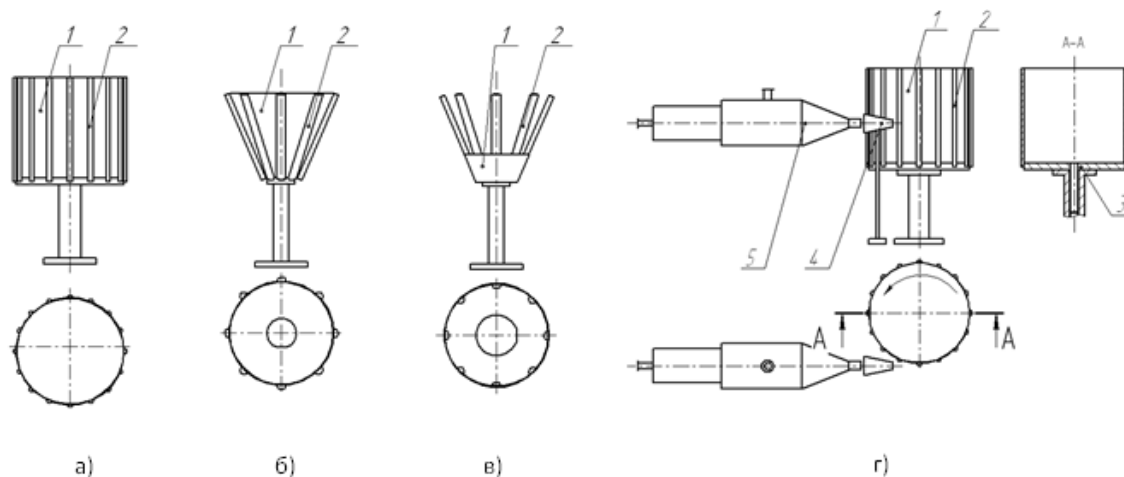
Варианты конструкции диспергатора. 1 — полое тело; 2 — полуцилиндрические стержни; 3 — подвижная платформа; 4 — щелевой элемент; 5 - эжектор; а - диспергатор цилиндрической формы с нарифлениями снаружи на неподвижной платформе; б - диспергатор конической формы с нарифлениями снаружи на неподвижной платформе; в - диспергатор конической формы с нарифлениями внутри на неподвижной платформе; г - диспергатор цилиндрической формы с нарифлениями снаружи на подвижной платформе
